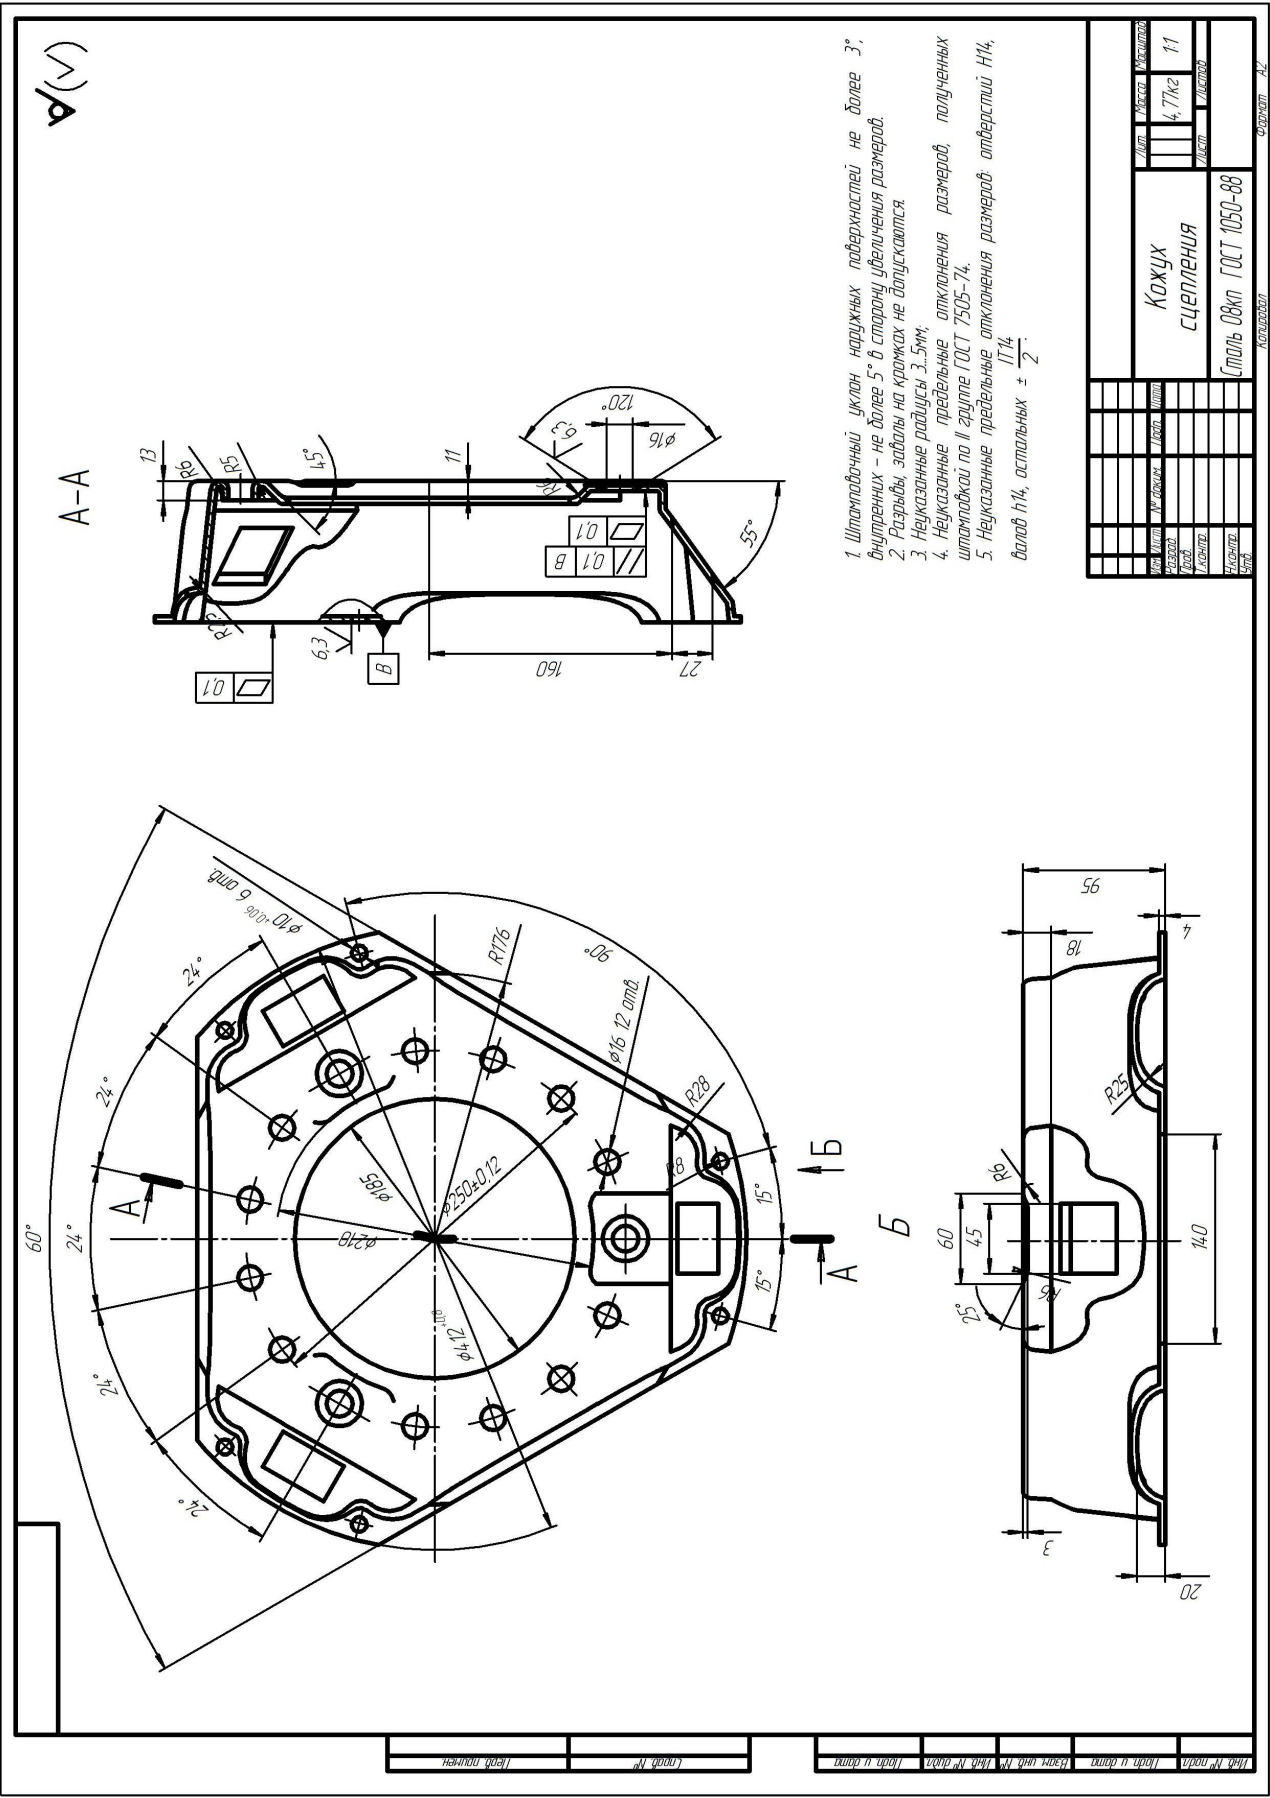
Пример выполнения рабочего чертежа кожуха сцепления
